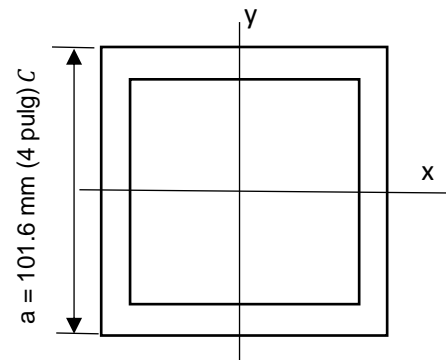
Vista lateral del área de soldadura.
